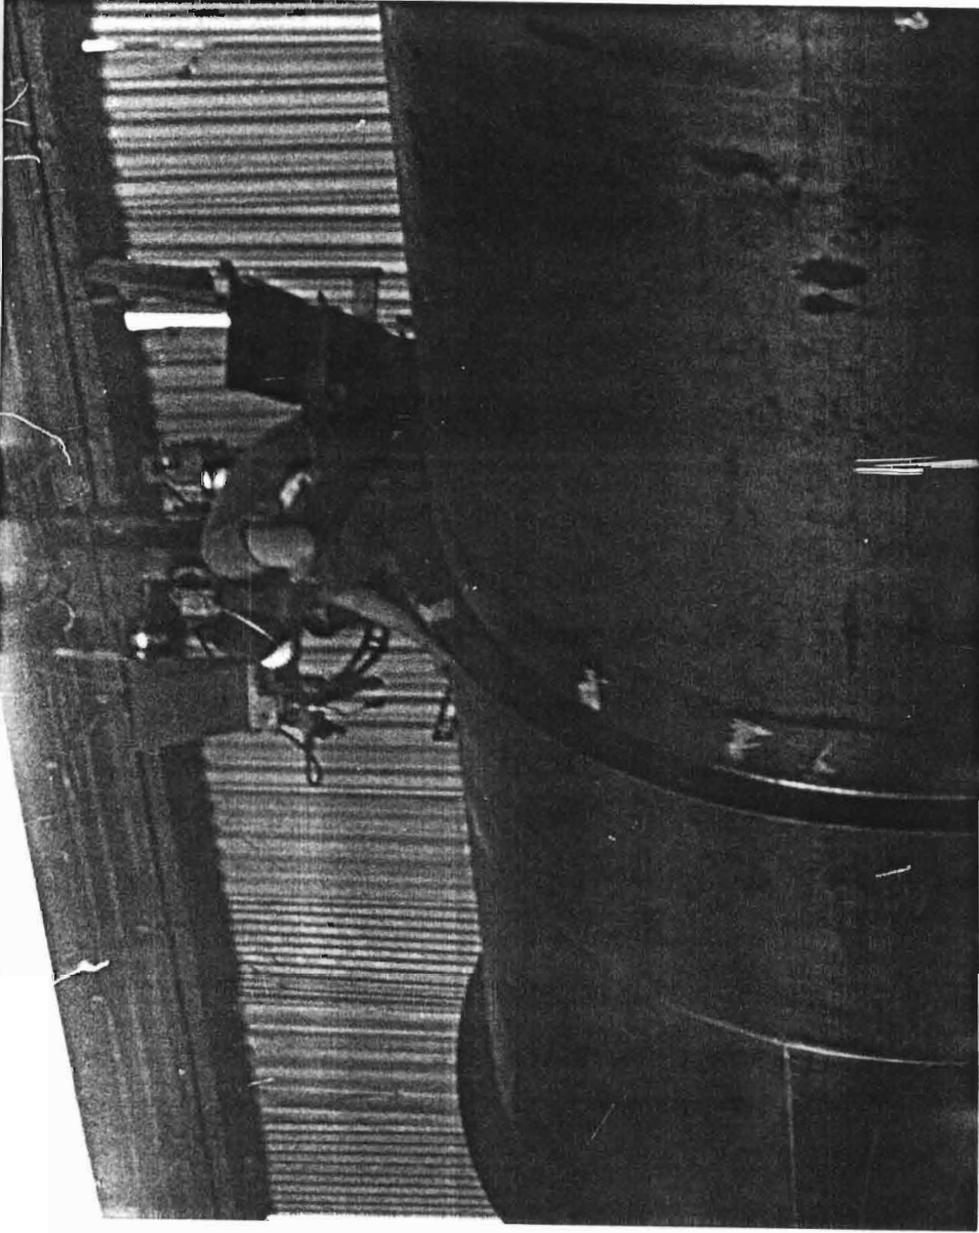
SOLDADURA RADIAL DE UN TUBO POR MEDIO DE ARCO SUMERGIDO
